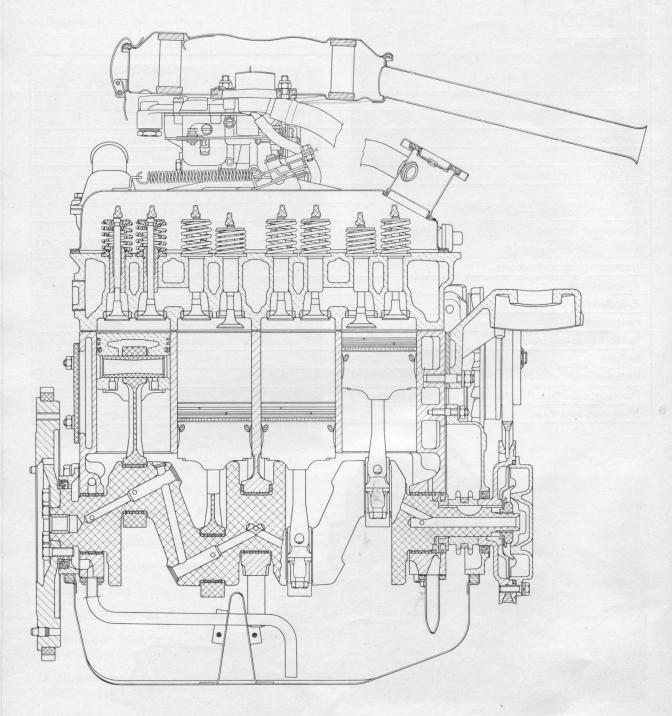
Längsschnitt des Motors durch die Zylinder.
